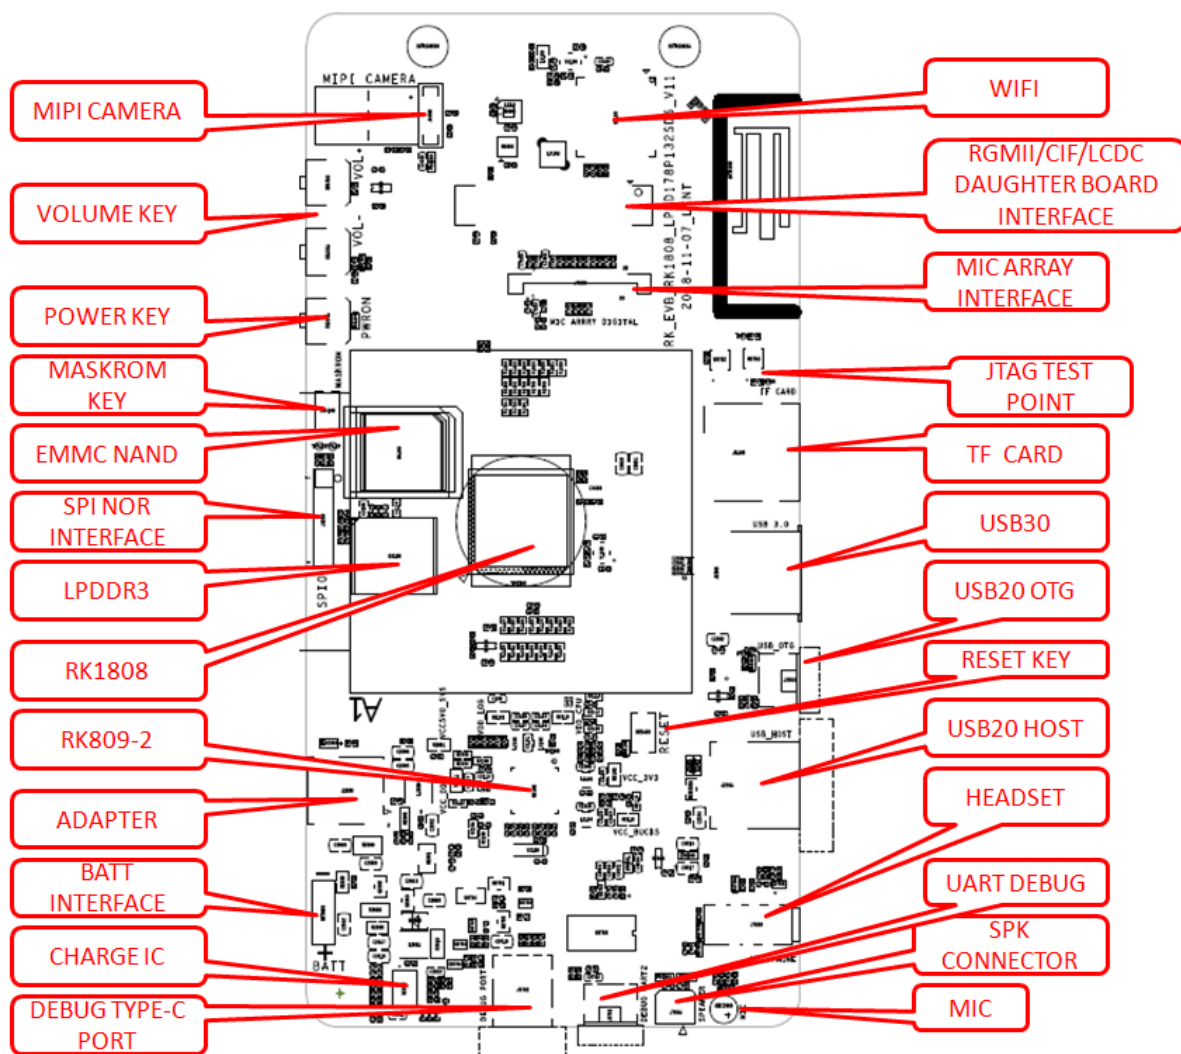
RK1808 EVB 1.1 PCB上TOP Layer模块布局位置图
